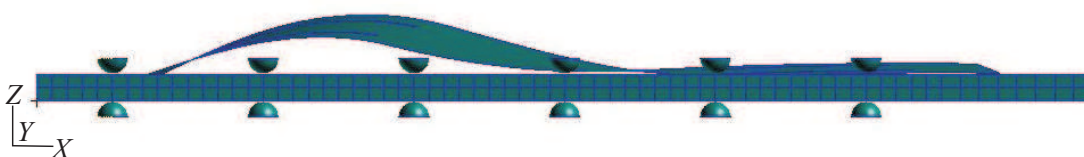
Конечно-элементная модель заготовки и поверхность с заданной кривизной (вид сбоку)
